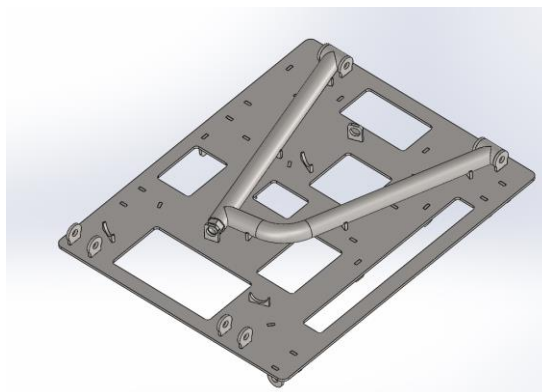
Utillaje/plantilla para soldadura de brazos de suspensión
